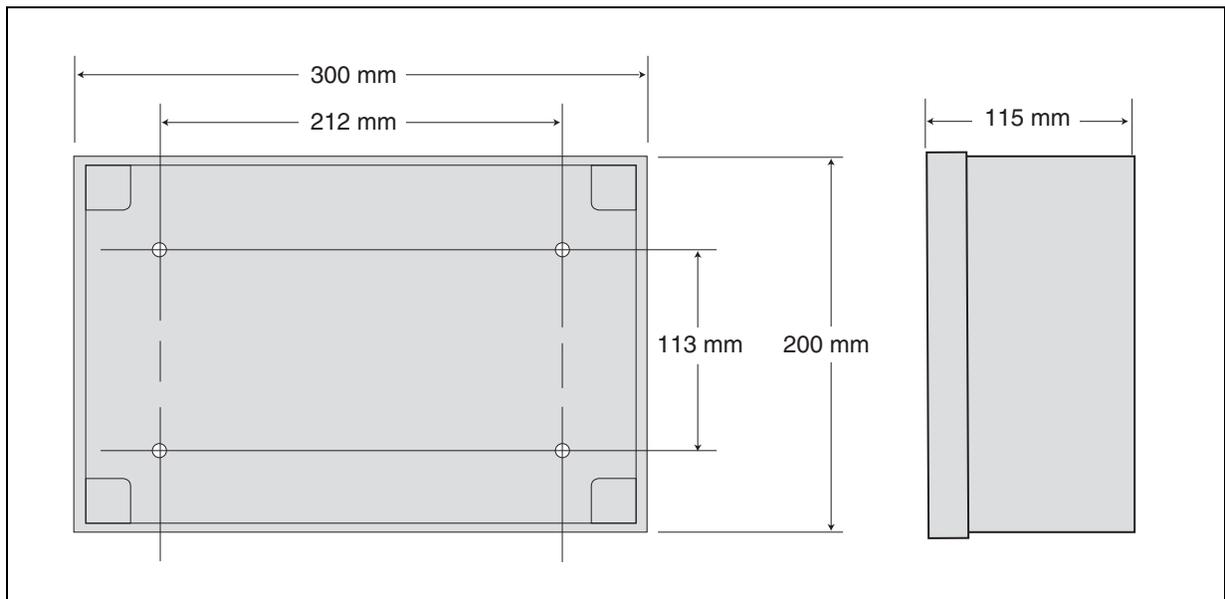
Caixa de Terminais TLS – Dimensões Gerais e de Fixação
